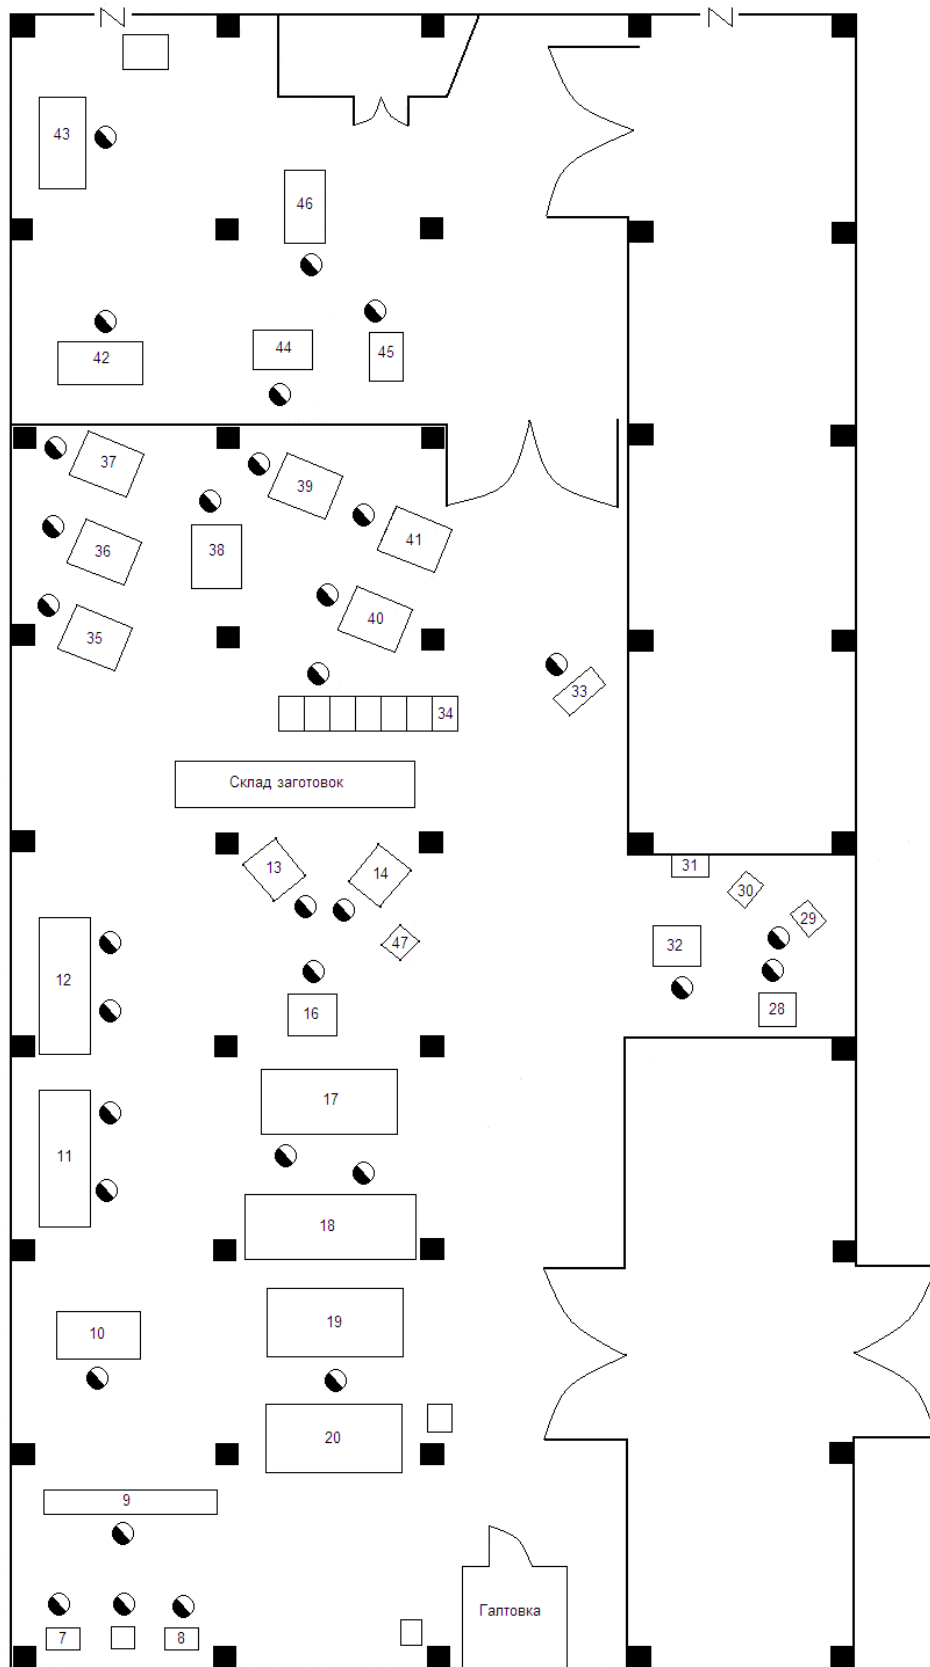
Цех №11 механічної і термічної обробки ріжучого інструменту.
